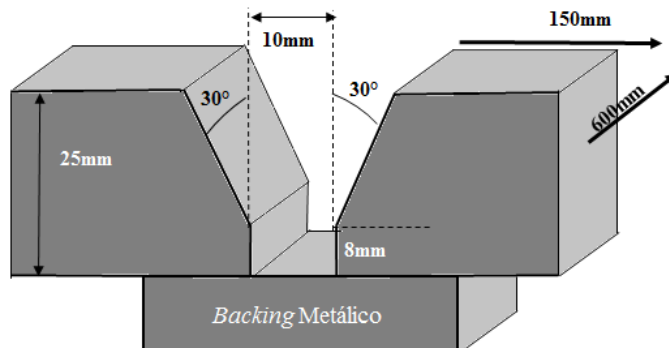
Representação esquemática do corpo de prova preparado para a soldagem e dimensões do chanfro.
